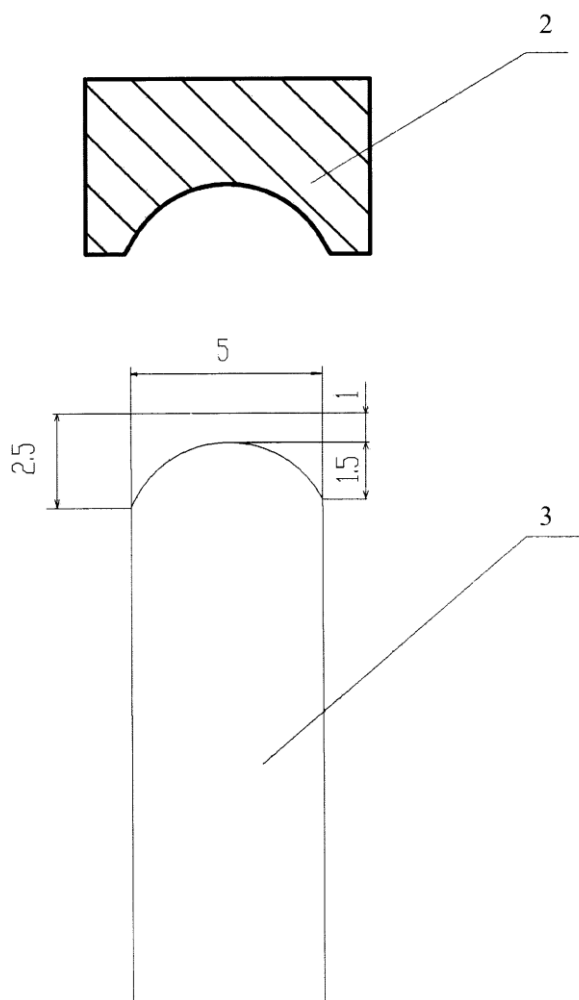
Схема, показывающая поверхность заготовки, обрабатываемой с помощью кольцевого желоба
